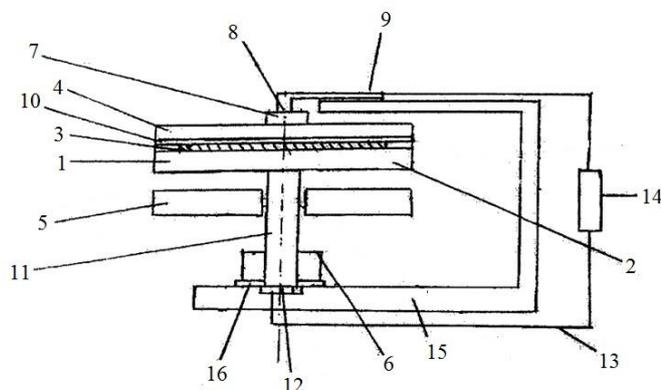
Солнечный магнитный двигатель с двумя скользящими контактами к токовыводу генератора и к оси ротора
